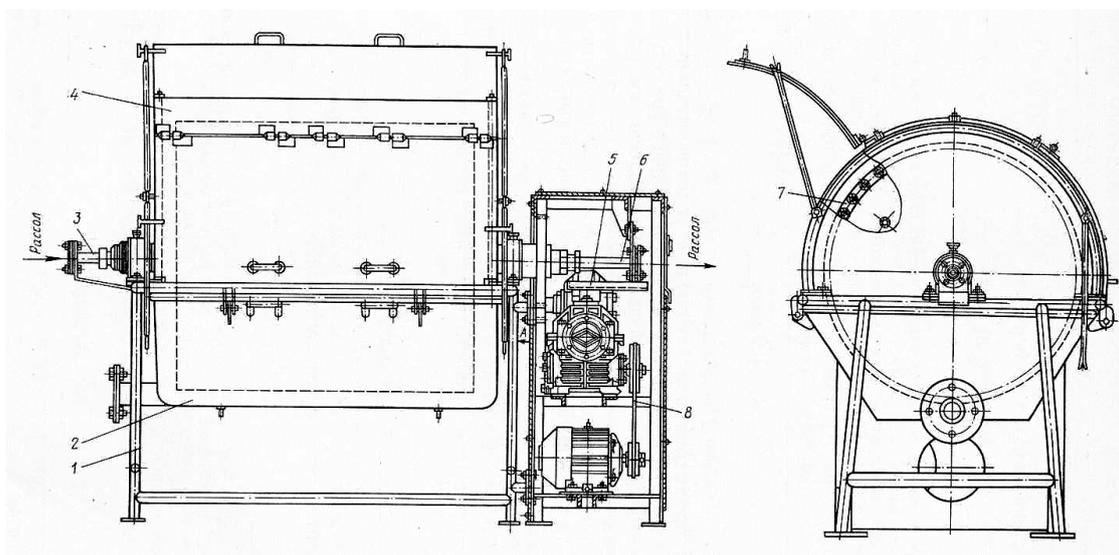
Установка для обезвоживания сгустка и охлаждения творога УПТ:
